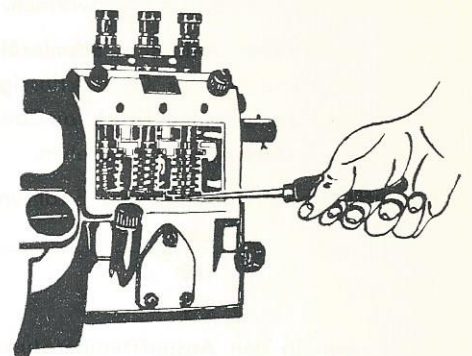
Entlüftung der Einspritzpumpe. Vorpumpen zum Entlüften der Druckleitungen
